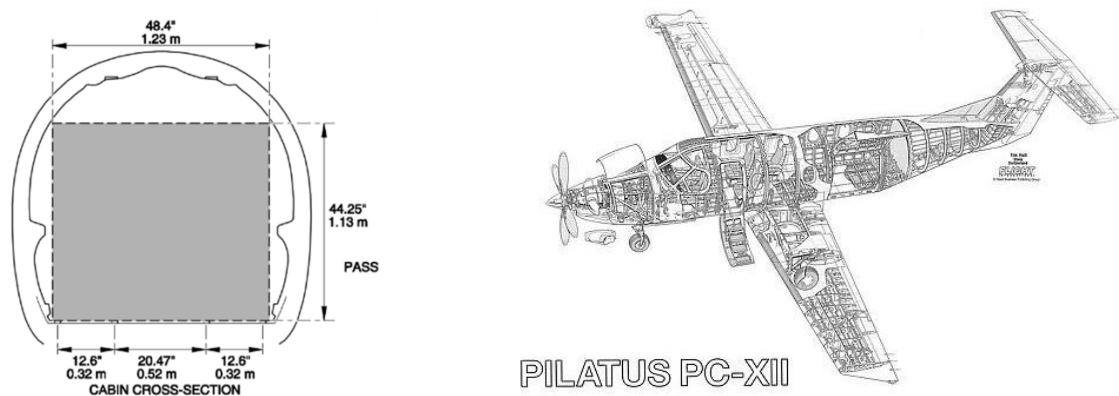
Corte transversal de la cabina de pasajeros [6] y vista interior 3D del Pilatus PC-12 [69]
